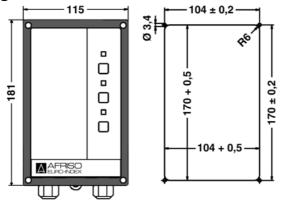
Leckanzeigegerät mit Montagerahmen für den Einbau in Schalttafeln; rechts: Schalttafelausschnitt
